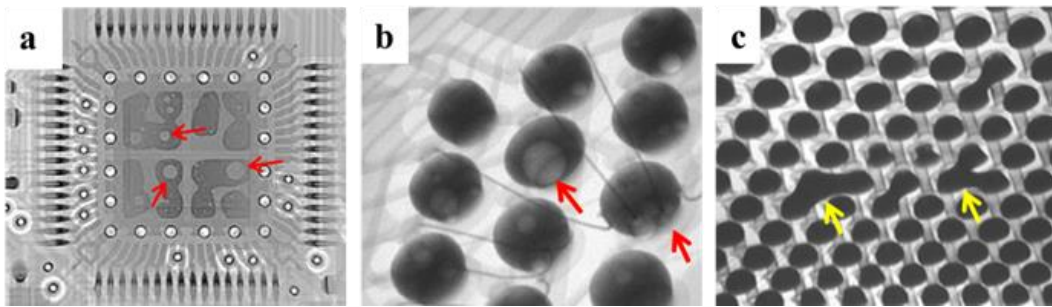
4. Défauts détectable seulement par AXI, a) défaut de bulles de gaz présentes dans la soudure sous un composant QFN; b) Défauts de bulle de gaz présentes dans les billes de soudure d'un BGA [60]; c) Défauts de court-circuit liant plusieurs billes de soudure d'un BGA;
